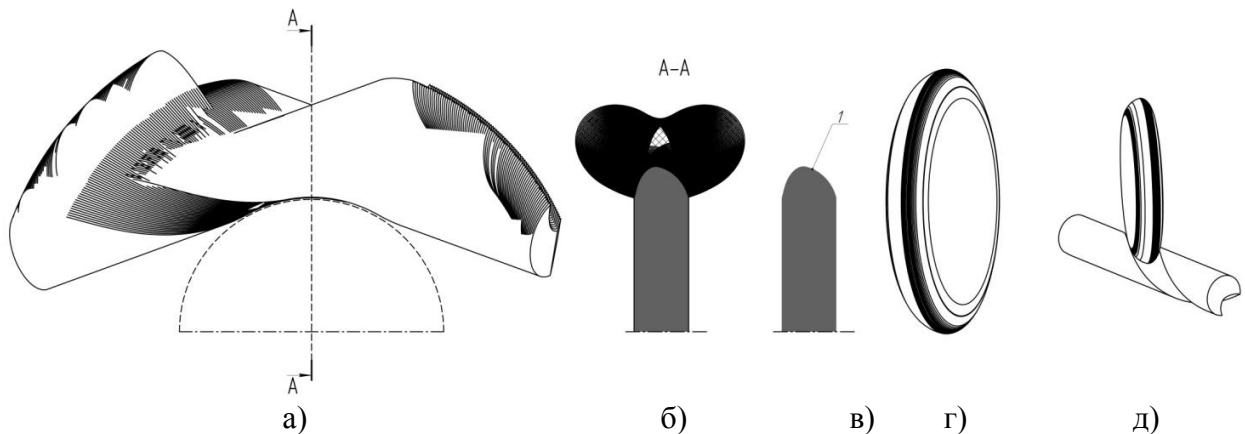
Знаходження геометричних параметрів ВПІ інструменту для обробки гвинтової поверхні свердла.
